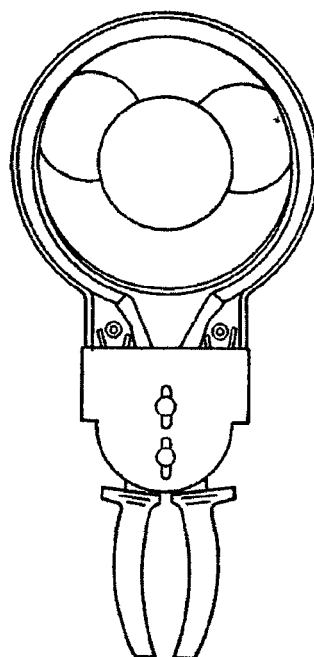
Приспособление И801.08.000 для снятия и установки поршневых колец
